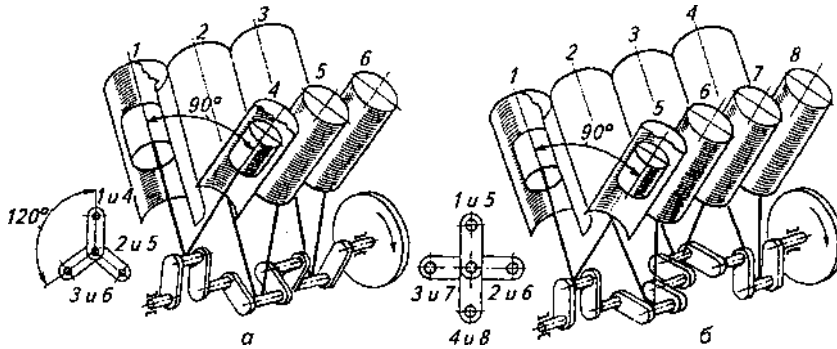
Схемы кривошипно-шатунных механизмов четырехтактных V-образных двигателей: а — шестицилиндрового; б — восьмицилиндрового; 1...8 — цилиндры.
